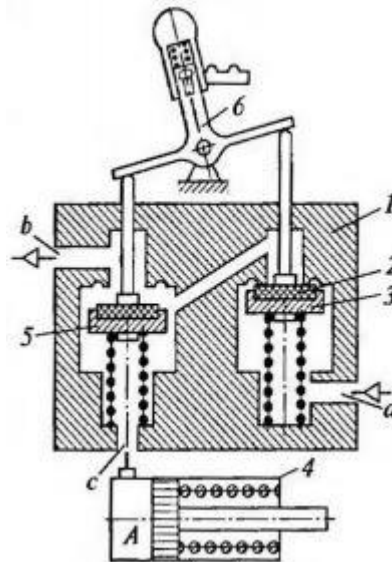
Пневматический клапанный распределитель: 1 - корпус; 2 - прокладка; 3,5 - клапаны; 4 - пневмоцилиндр; 6 - рукоятка управления.
